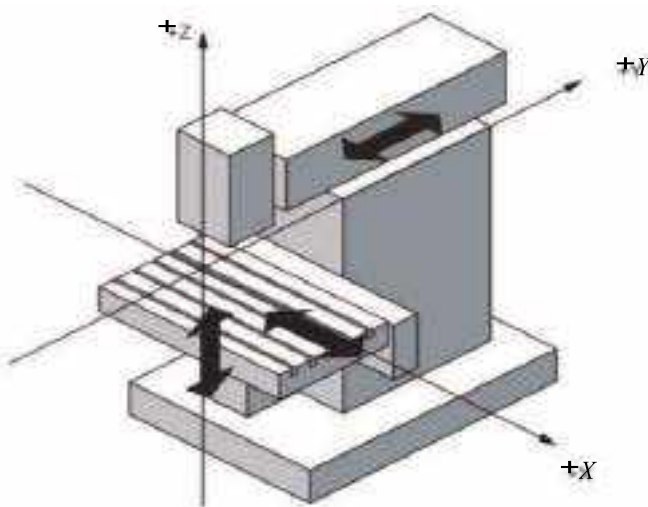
Направление координатных осей фрезерного станка с ЧПУ
